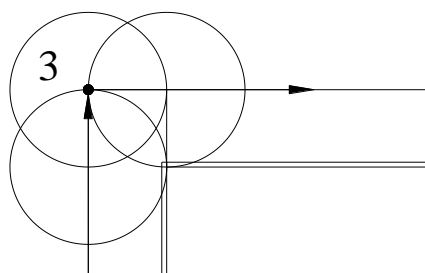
Схема отрыва и врезания инструмента при фрезеровании контура заготовки детали
